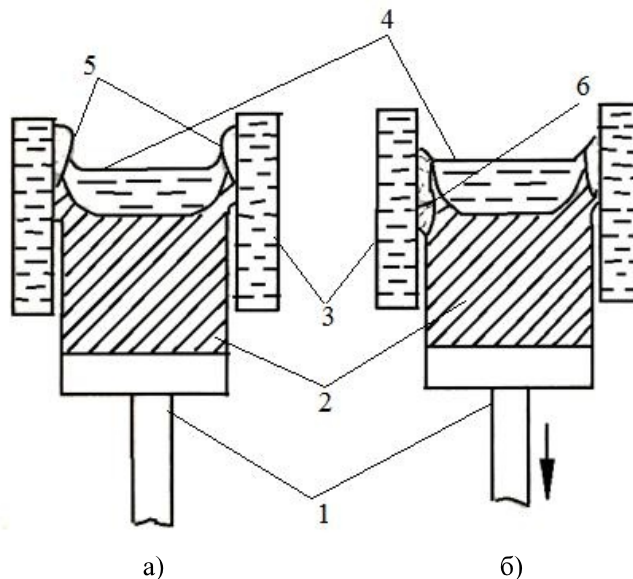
Схема утворення поперечних тріщин при витягуванні зливка з кристалізатора електронно-променевої печі: а — утворення корони над зливком при наплавленні; б — поява тріщин на поверхні зливка при витягуванні; 1 — механізм витягування зливка; 2 — зливко; 3 — кристалізатор; 4 — розплав металу; 5 — корона; 6 — тріщина, що утворена під час витягування.
